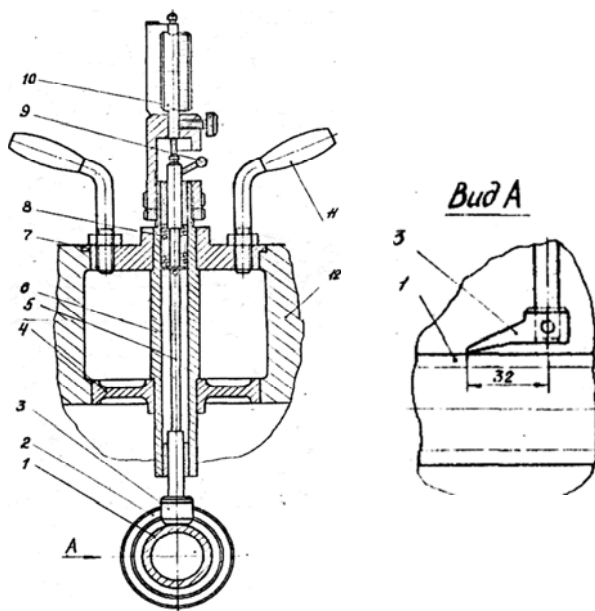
Приспособление для проверки перпендикулярности оси цилиндра к оси коленчатого вала двигателя:
